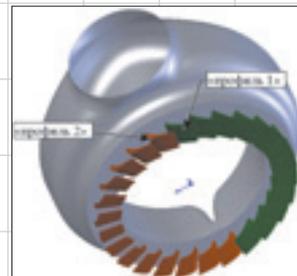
Модель газоприемного корпуса с сопловыми лопатками
